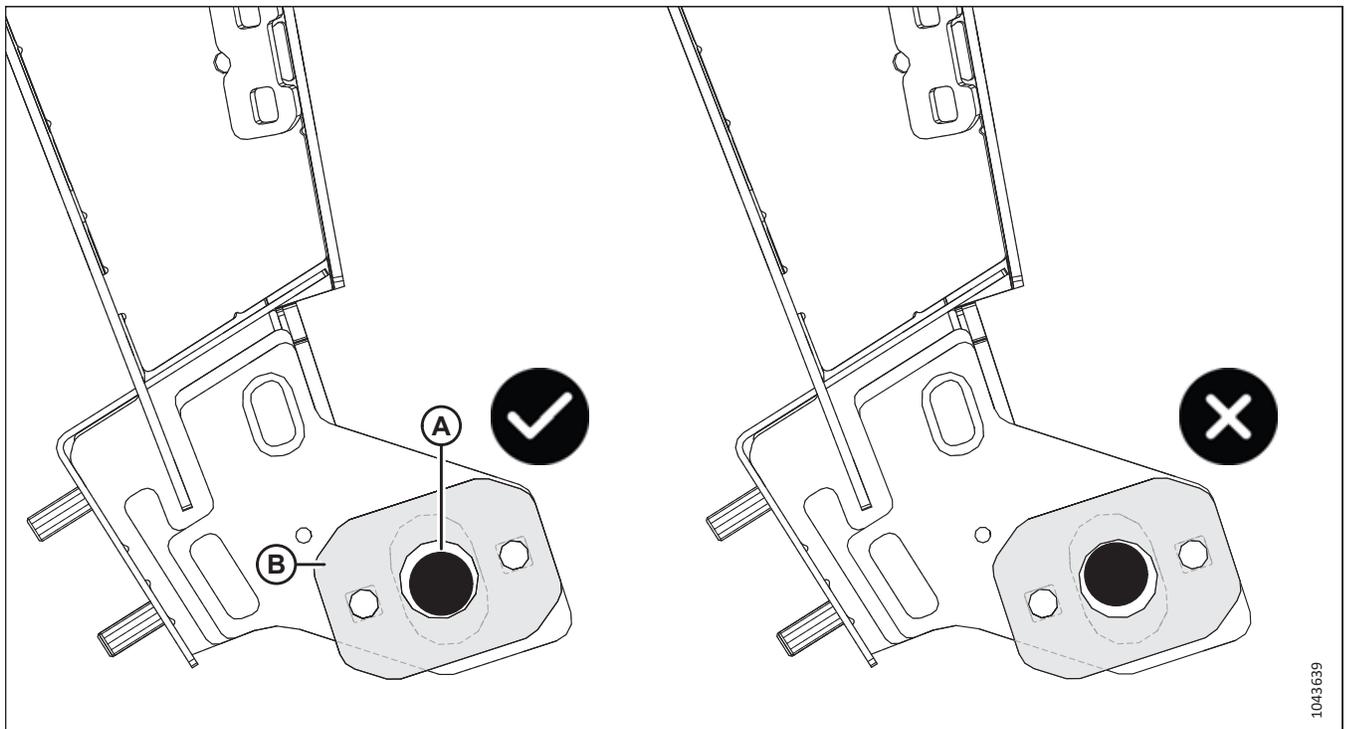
Alignement de la goupille de verrouillage du convoyeur sur une moissonneuse-batteuse John Deere de série X9 ou S7 – Plaque de réglage à position unique
